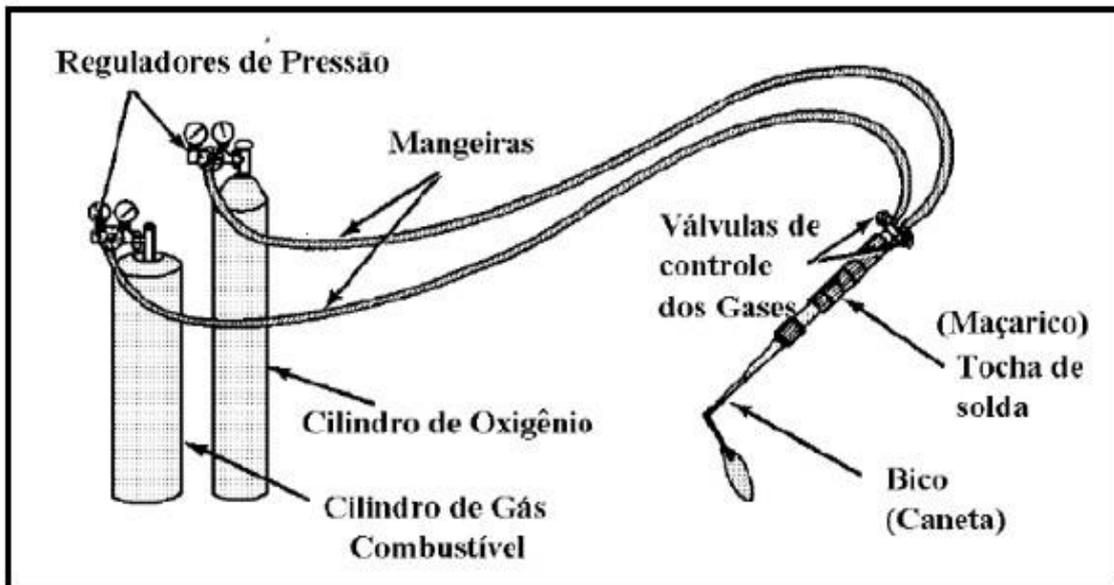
Esquema completo de soldagem a gás. [Fonte: www.mmborges.com/processos/Uniao/uniao%20termica%20-%20soldagem.htm].
